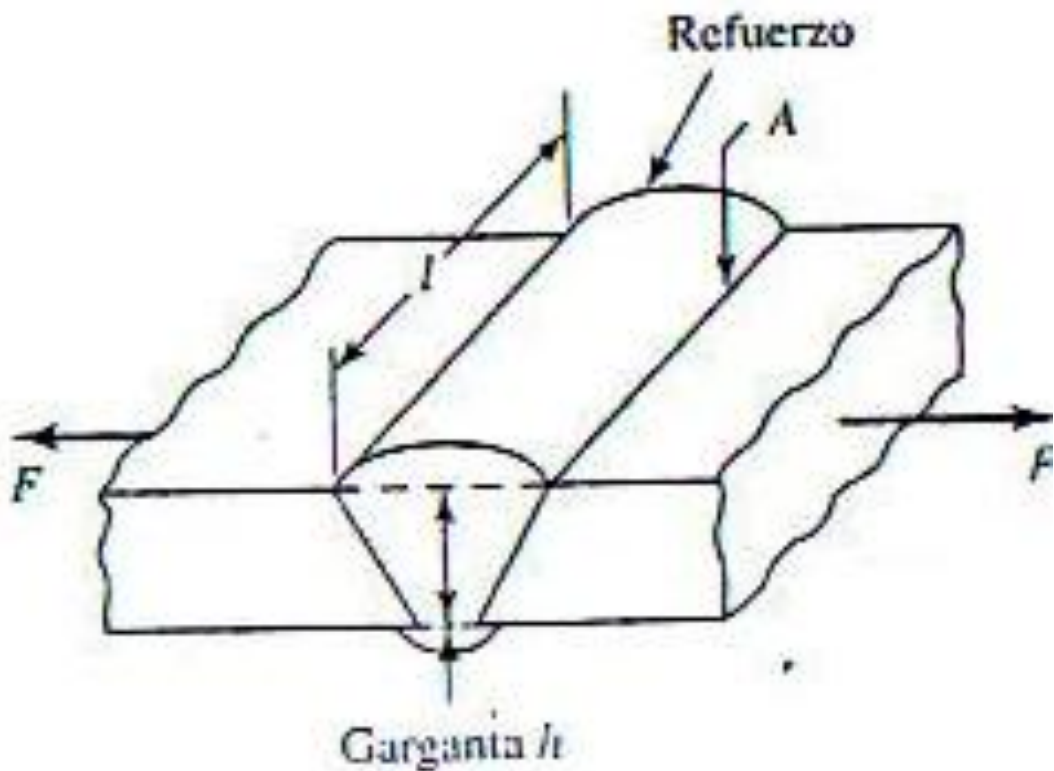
SOLDADURA A TOPE (Ref. 7)
